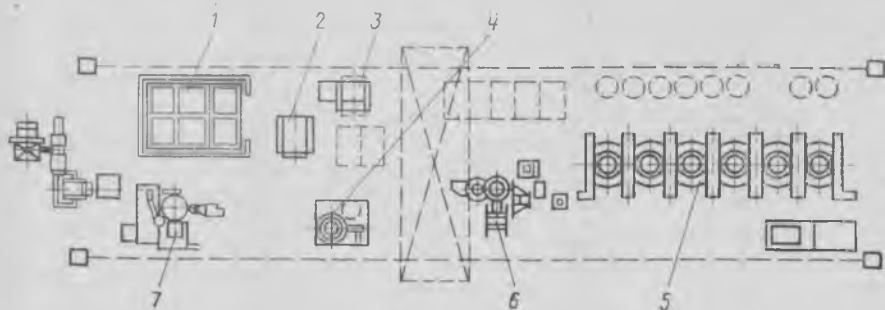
Схема полигона по изготовлению труб со стальным цилиндром
